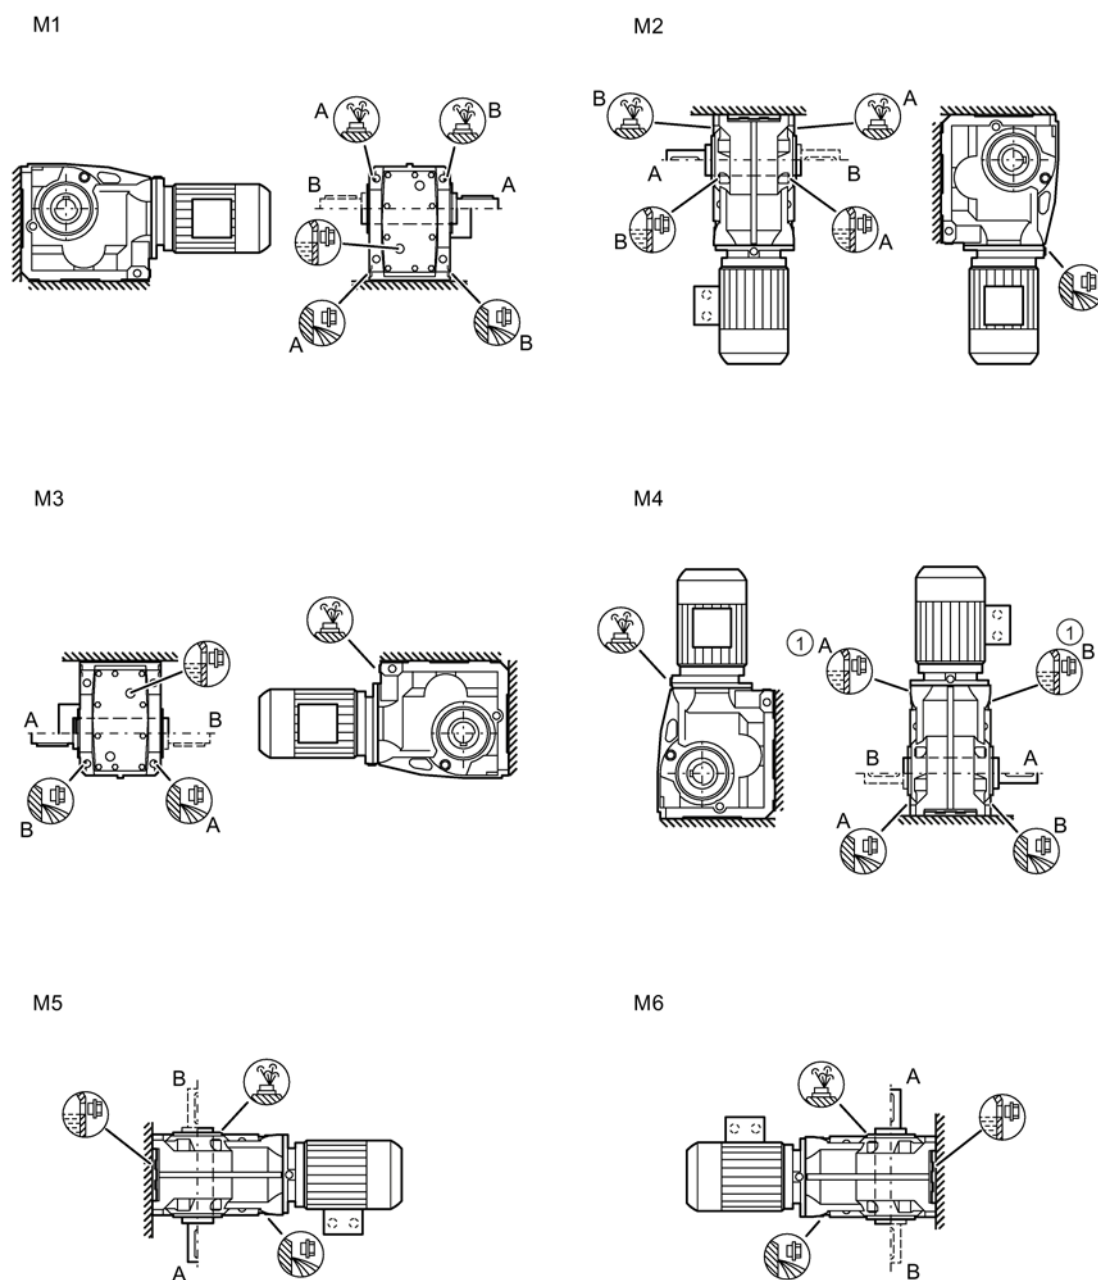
Монтажные положения для конического редуктора К. в исполнении на лапах, типоразмеры 39-189
